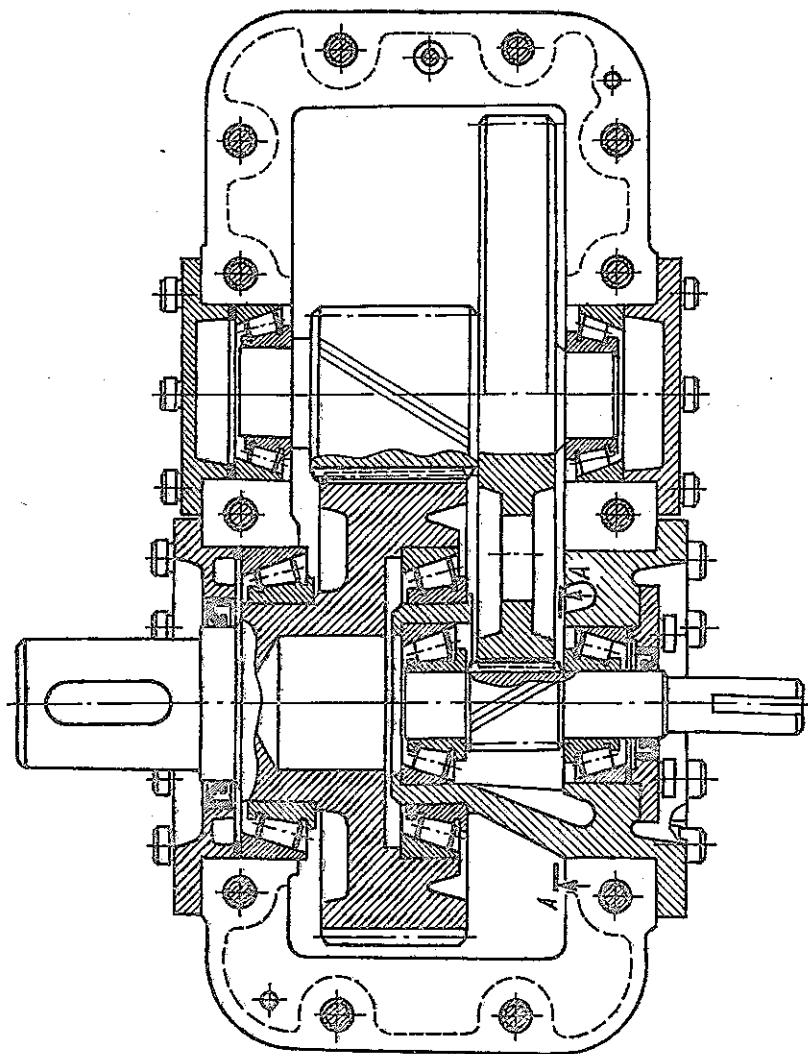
Двухступенчатый редуктор с соосными валами без внутренней стенки в корпусе
